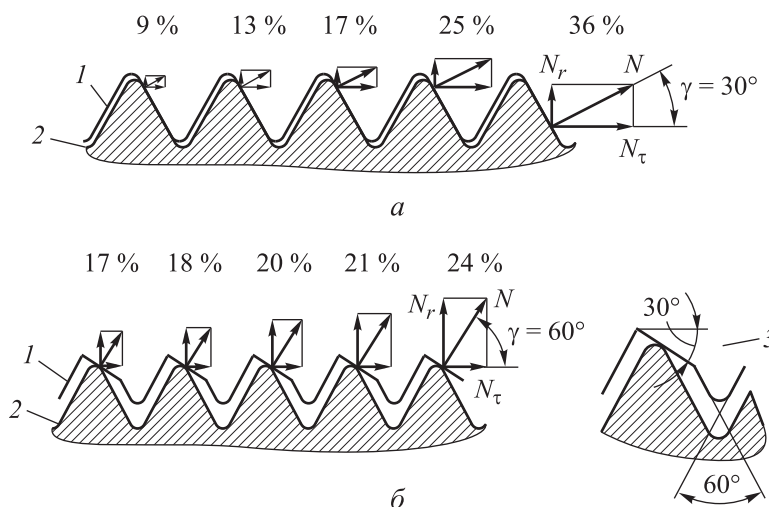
Распределение усилия затяжки F_a , %, по пяти виткам метрической (а) и самоstopорящейся (б) резьб гайки: 1 и 2 — резьбы гайки и болта; 3 — клиновидный выступ
